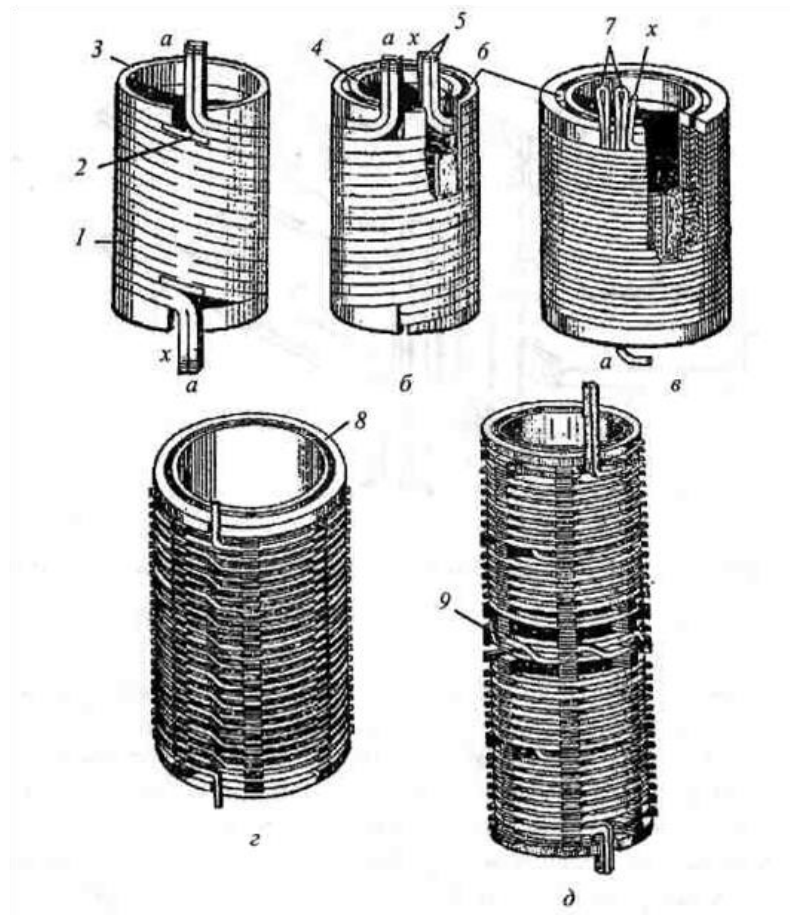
Циліндричні обмотки силових трансформаторів: а - одношарова; б - двошарова; в - багат шарова; г - безперервна; д - гвинтова
